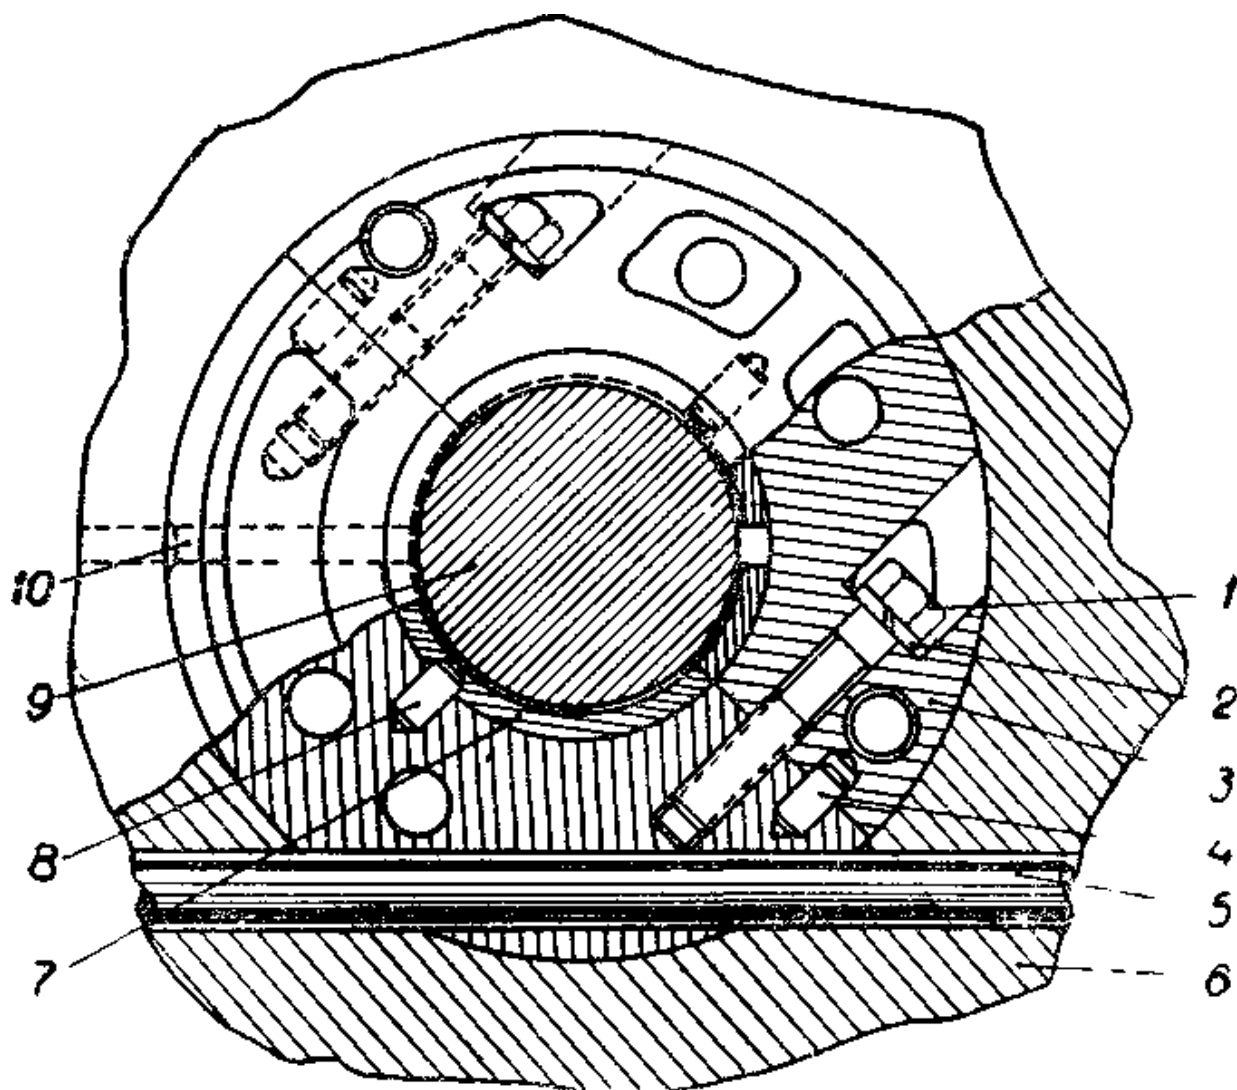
Опора среднего коренного подшипника (вид со стороны носка коленчатого вала)
